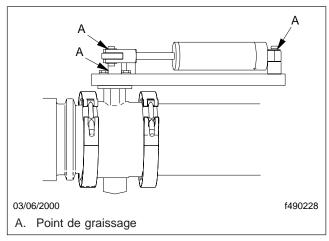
, Frein sur échappement et cylindre pneumatique Pacbrake
